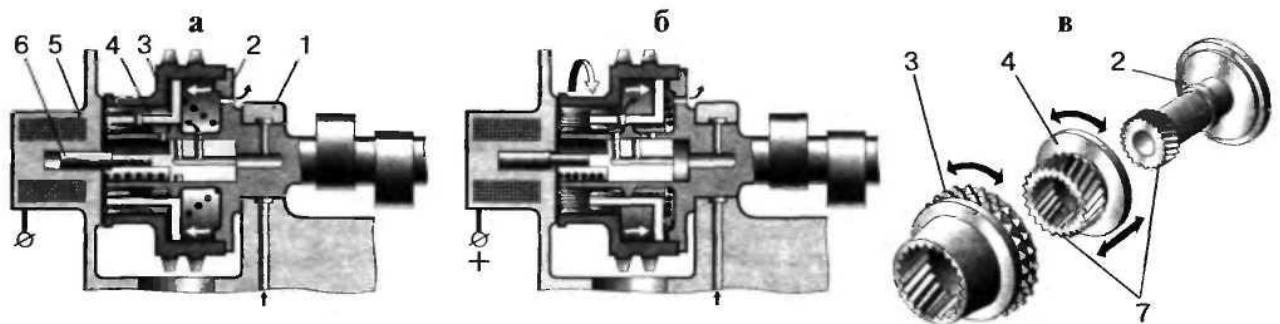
Візуалізація технічного рішення пристрою зміни фаз впуску та випуску газорозподілу: 1 - головка блоку; 2 - розподільчий вал; 3 - зірочка приводу розподільного вала; 4 - поршень; 5 - соленоїд; 6 - явір-клапан; 7 - косозубі шліци а - пізні фази - електромагніт виключений, поршень віджаний уліво тиском мастила, що надходить через клапан; б - ранні фази - електромагніт переводить клапан уліво, поршень тиском мастила переміщається вправо, провертаючи зірочку щодо розподільного вала; в - з'єднання деталей пристрою косозубими шліцами
